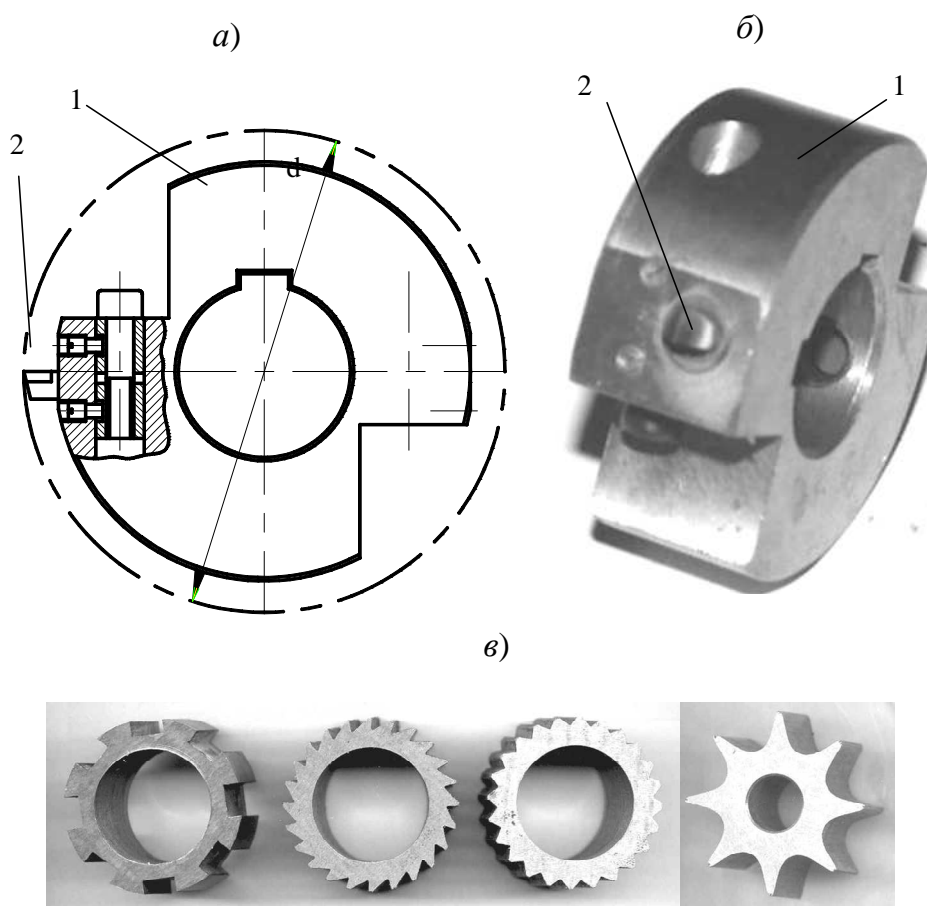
Конструкция резцовой головки (а, б) и образцы деталей (в) с зубчатым контуром на наружной поверхности:
